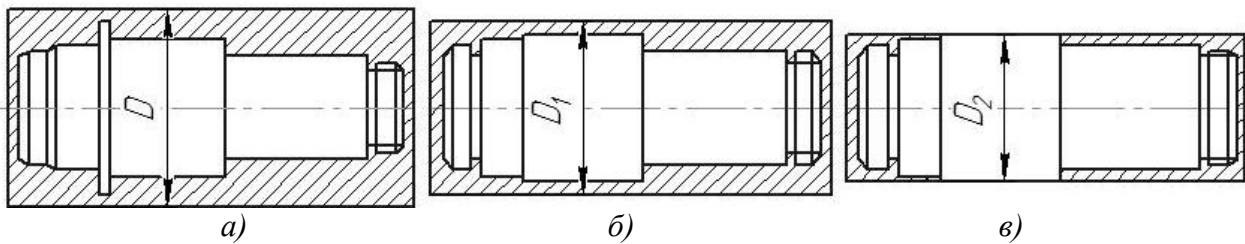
Види конструкцій валів з різним об'ємом матеріалу, який знімається при токарній обробці:
